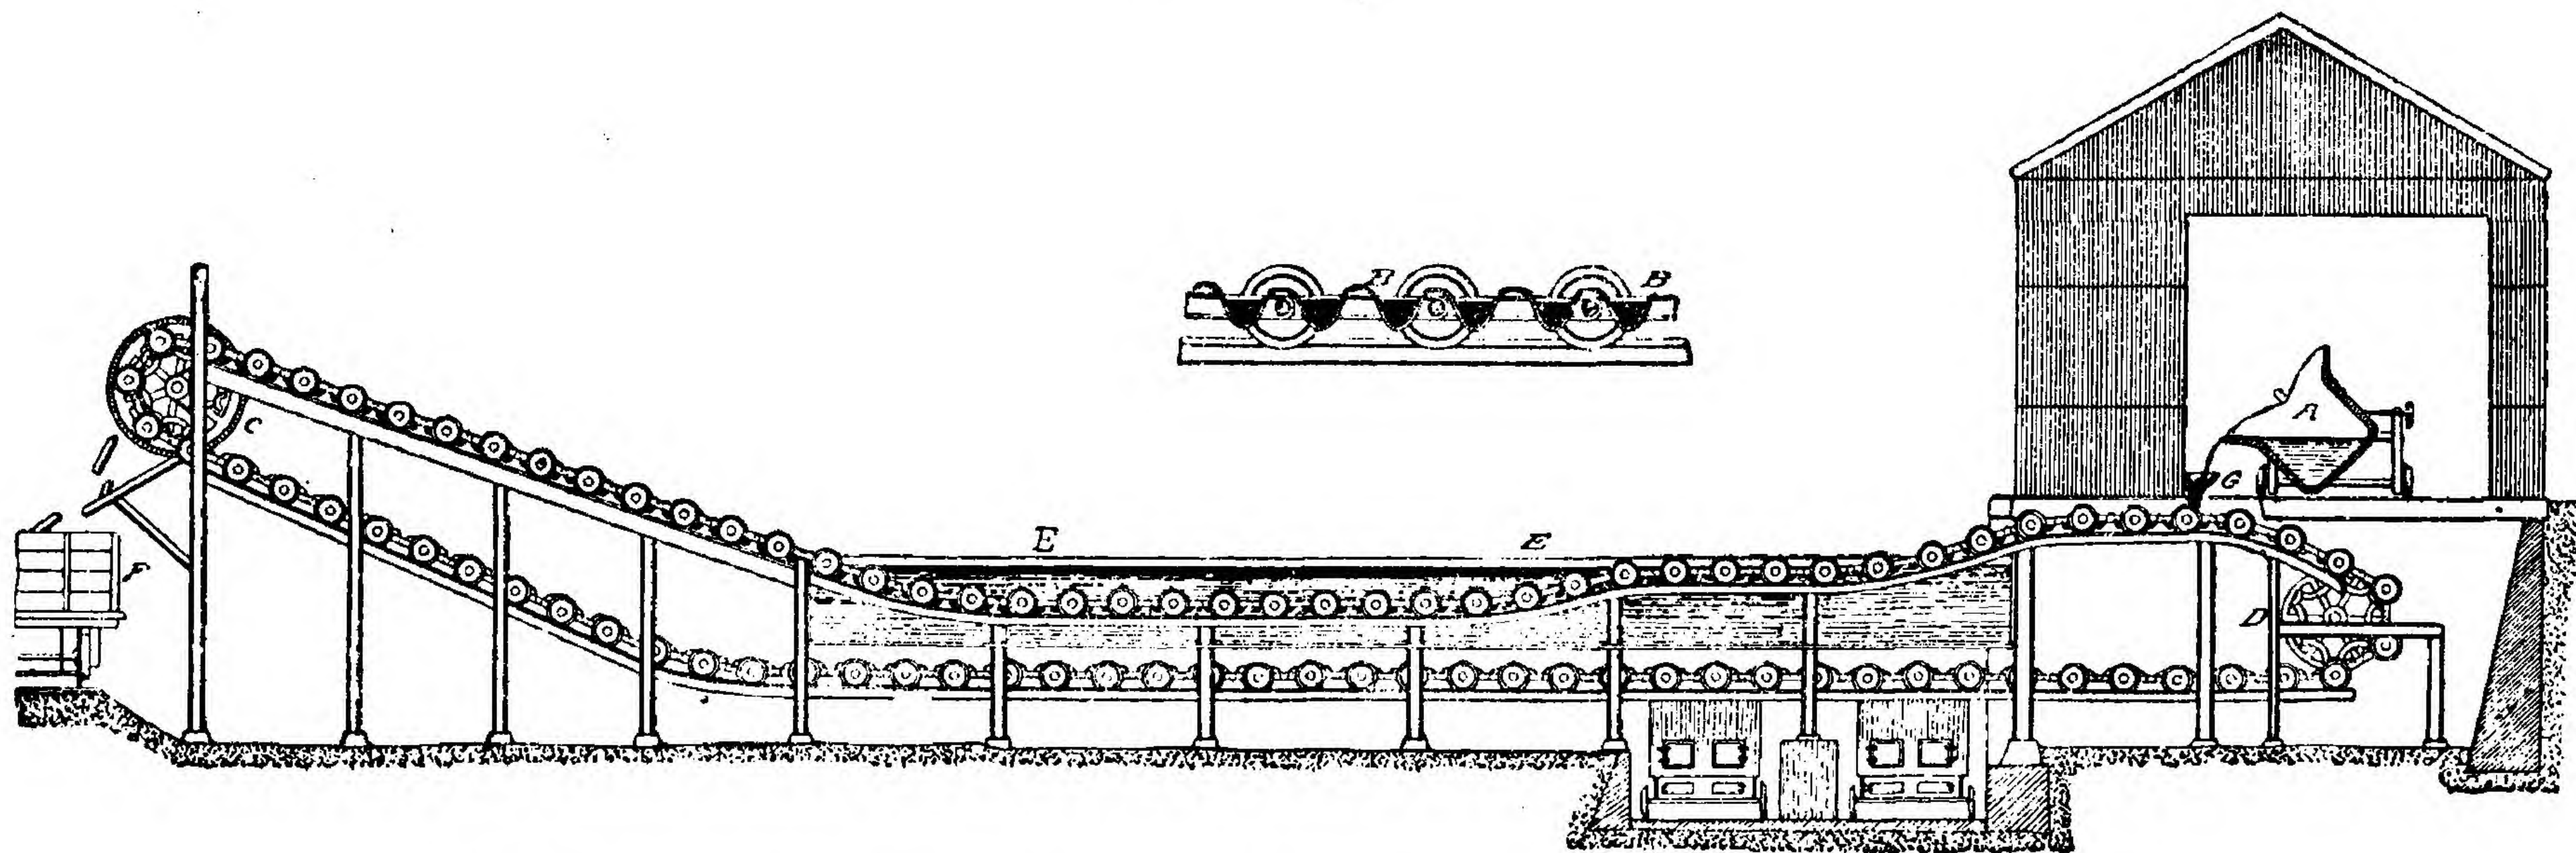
Схематическій чертежъ аппарата Uehling'a для отливки чугуна въ свинки.
